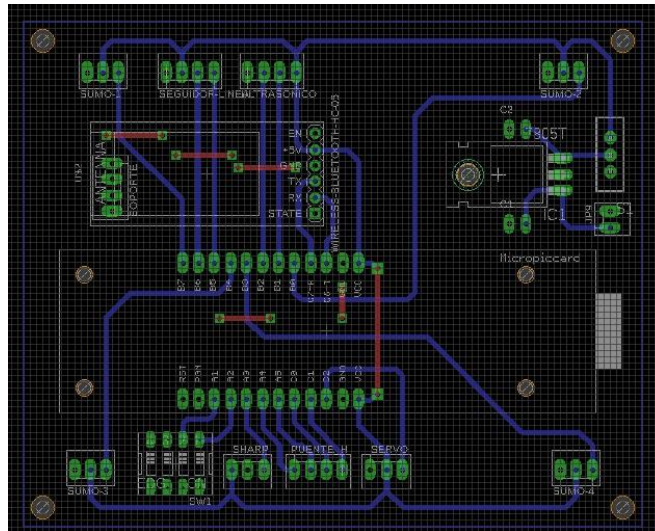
Diseño PCB de la tarjeta de control del mini robot.
